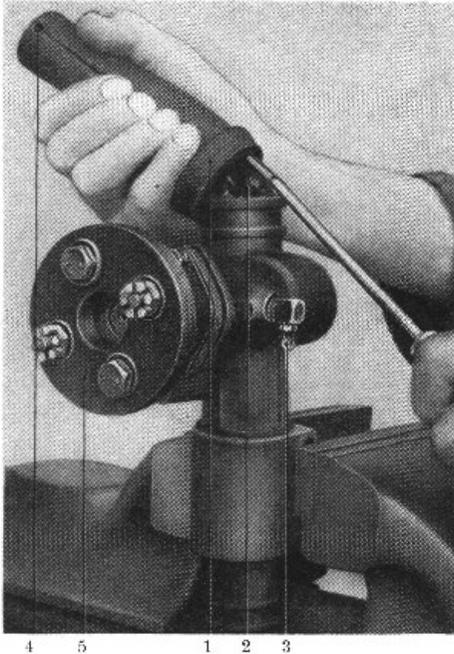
Lenkgehäuse mit Schmiermittel füllen
